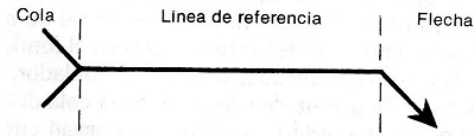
La cola, línea de referencia y la flecha, símbolo básico de la soldadura (Welding Society, 6ª. Ed., 1968, sección 1 p. 1.8).
